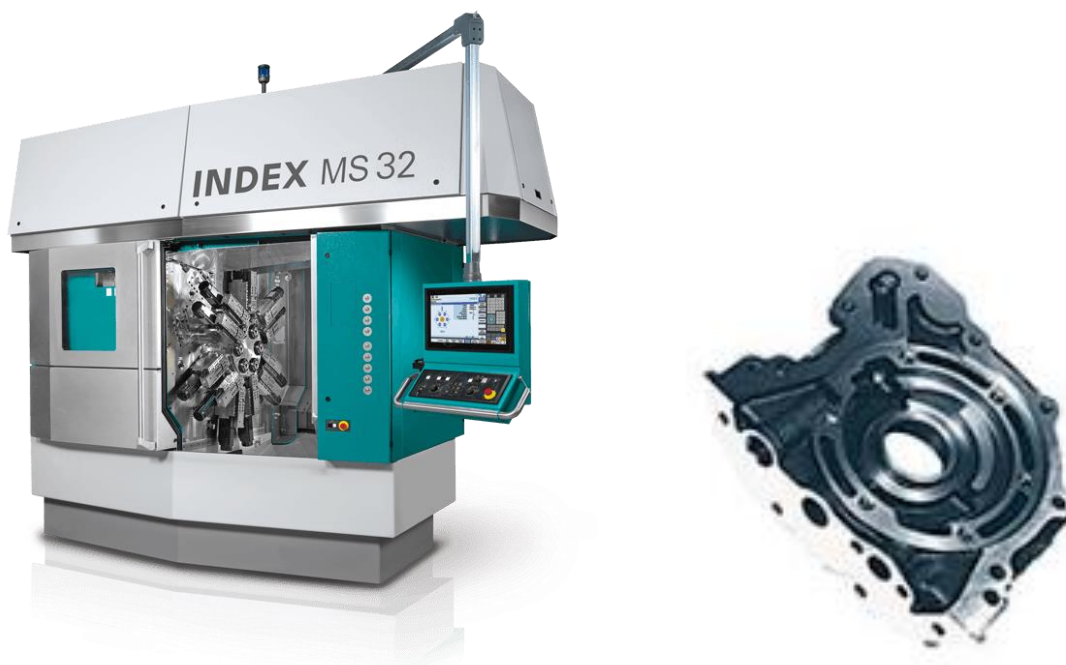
Багатошпиндельний токарний автомат INDEX MS32-6 фірми Kingsbury
